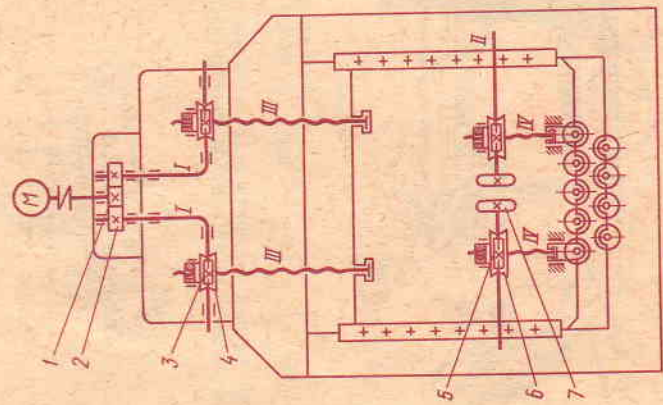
Кинематическая схема регулирования положения валков листопрямильной машины: 1, 2 — колеса редуктора, 3, 5 — червяки, 4, 6 — червячные колеса, 7 — маховик
